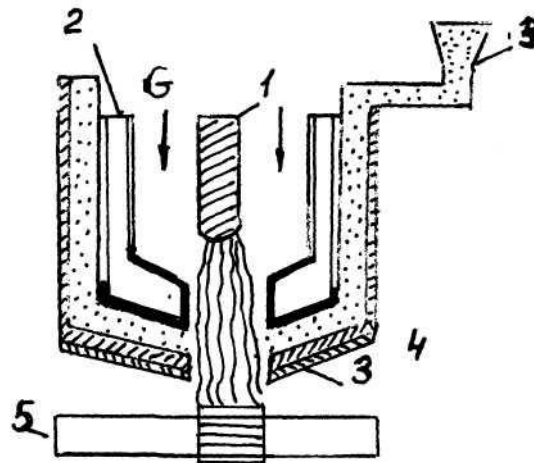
Схема установки для плазменного напыления: 1- катод ЭДП; 2- сопло, анод ЭДП; 3- наружное сопло; 4 – питатель порошка; 5- деталь; G – поток плазмообразующего газа поверхностью вставки.
